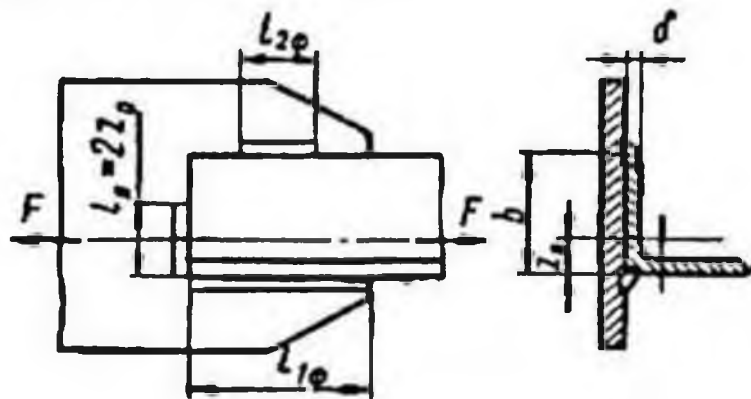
Сварное соединение уголка с косынкой
